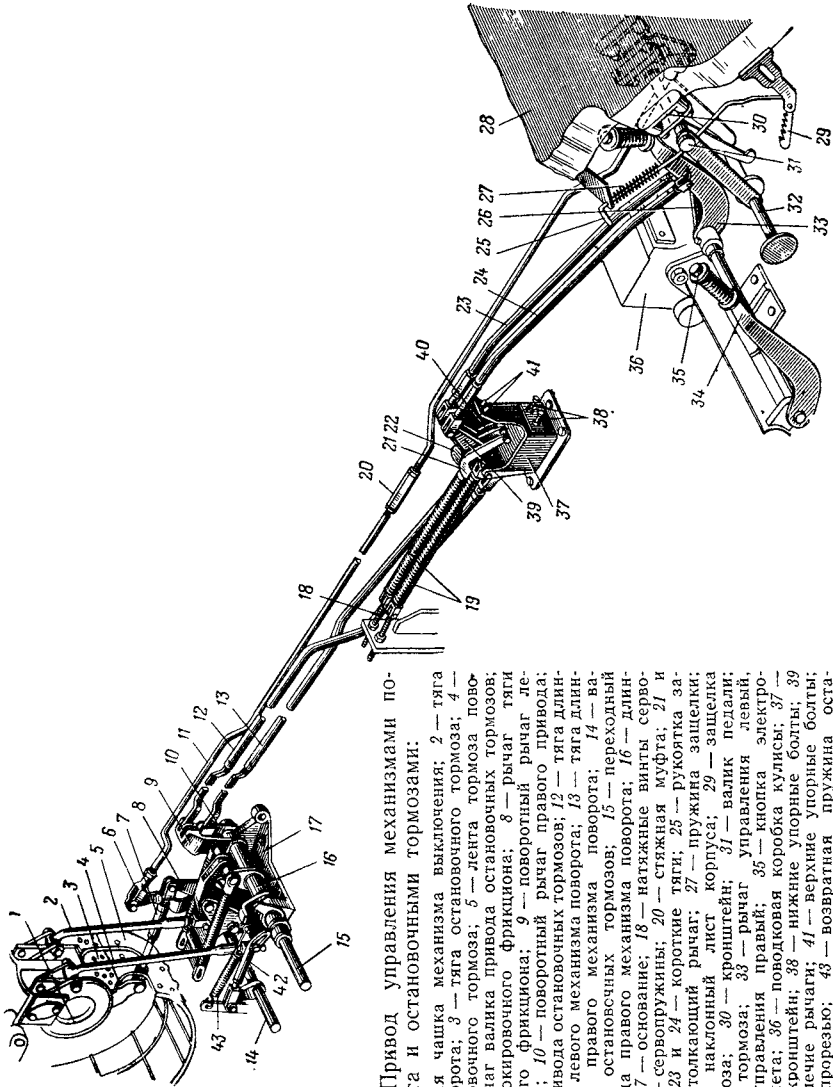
Привод управления механизмами поворота и остановочными тормозами:
